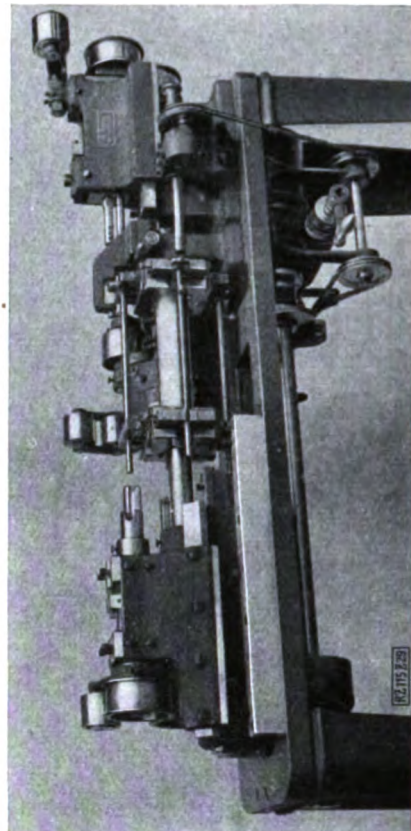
Maschine für die Bearbeitung der Hebe- und Schiebewellen, Abb. 30, nach Abb. 31 bis 33.
